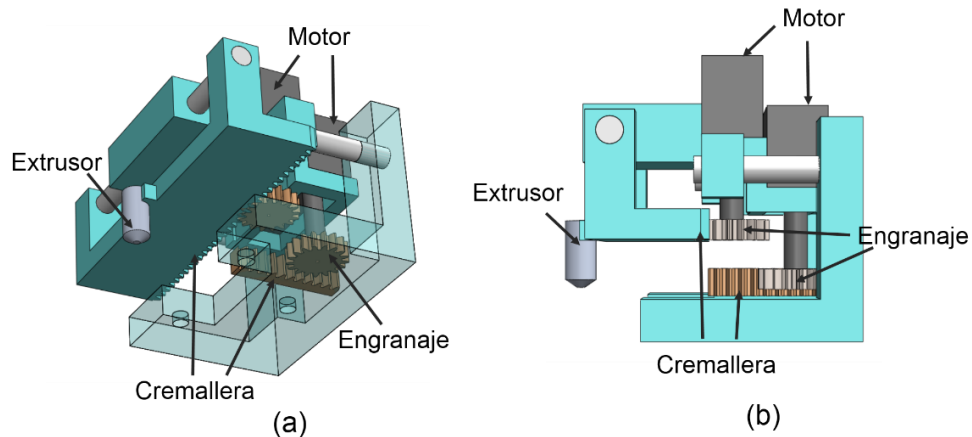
Partes que componen el sistema engranaje cremallera para mover el extrusor dentro del área de manufactura transversal a la columna. (a) Vista isométrica y (b) vista alzada.
